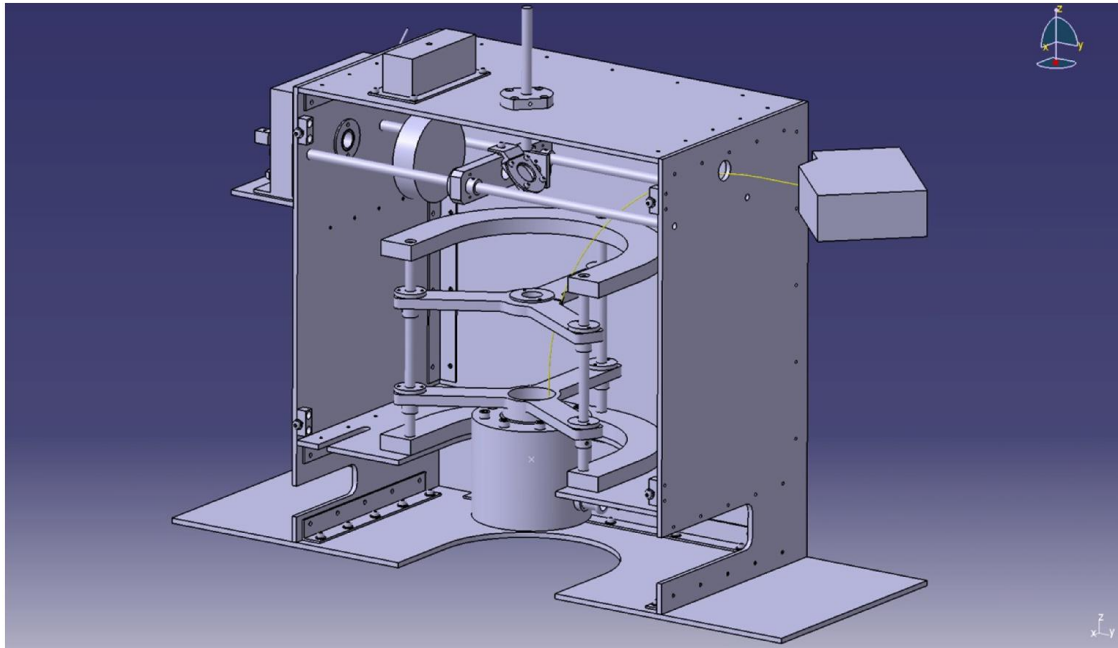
Dessin technique SolidWorks du boîtier optique. P. Pariset, LAC.
